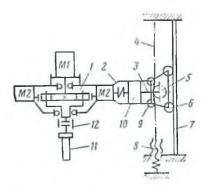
Кинематическая схема вращательно-подающего механизма станка 2СБР-125-30
